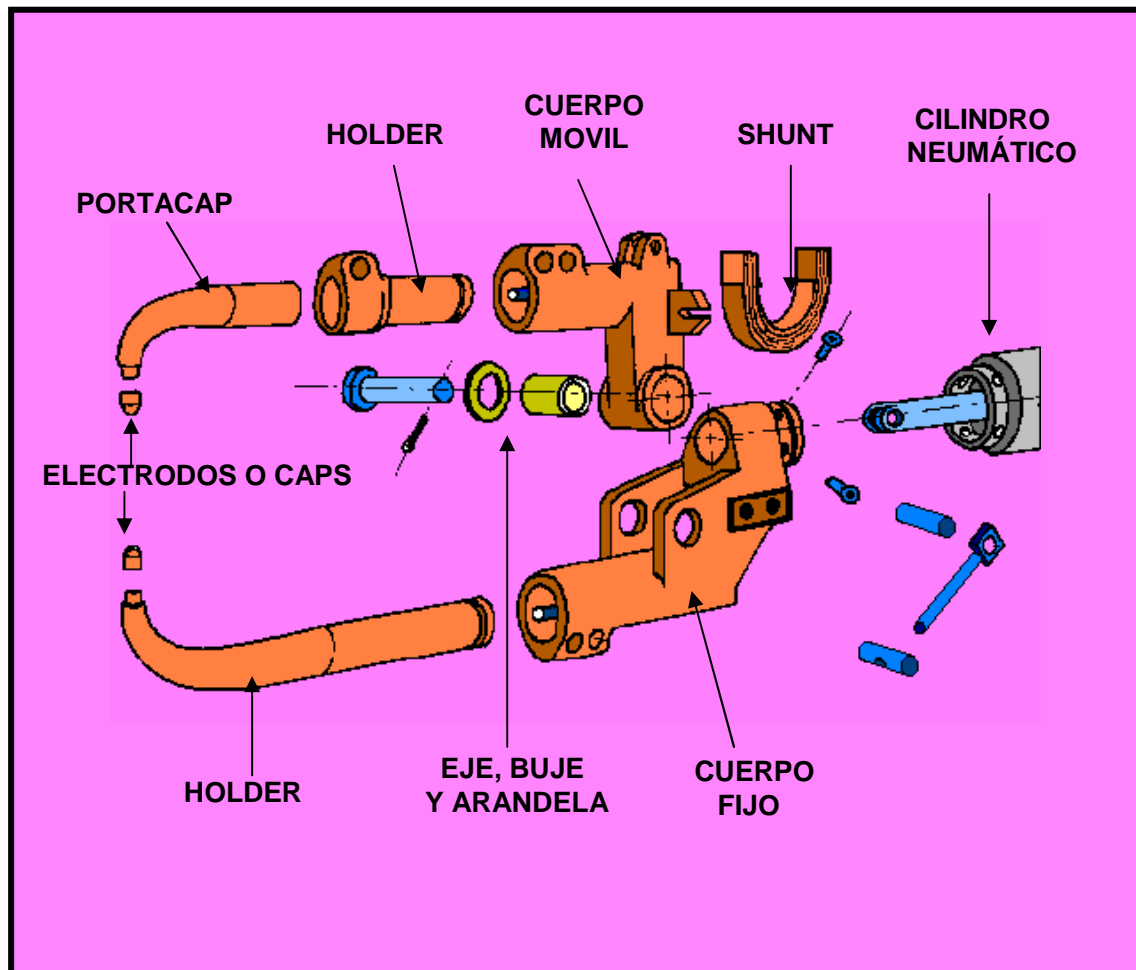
Despiece de una Soldadora Portable Tipo X.
